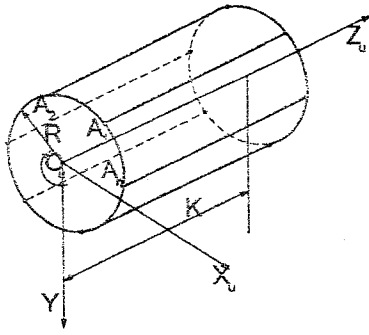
Концевая цилиндрическая фреза с прямолинейными зубьями
